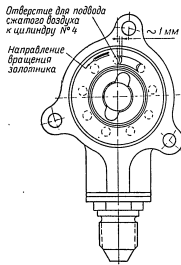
Схема установки золотника распределителя сжатого воздуха.
